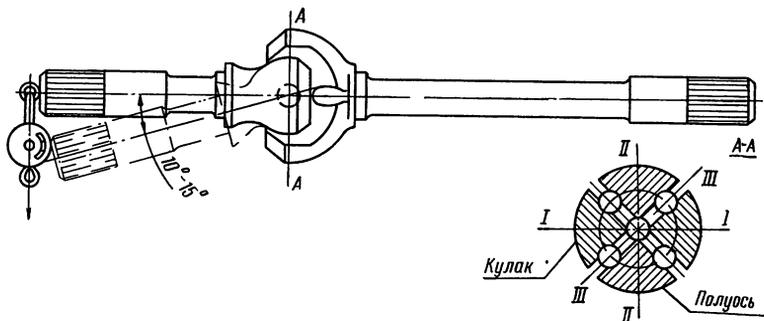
Схема проверки предварительного натяга шарнира полуоси переднего моста
